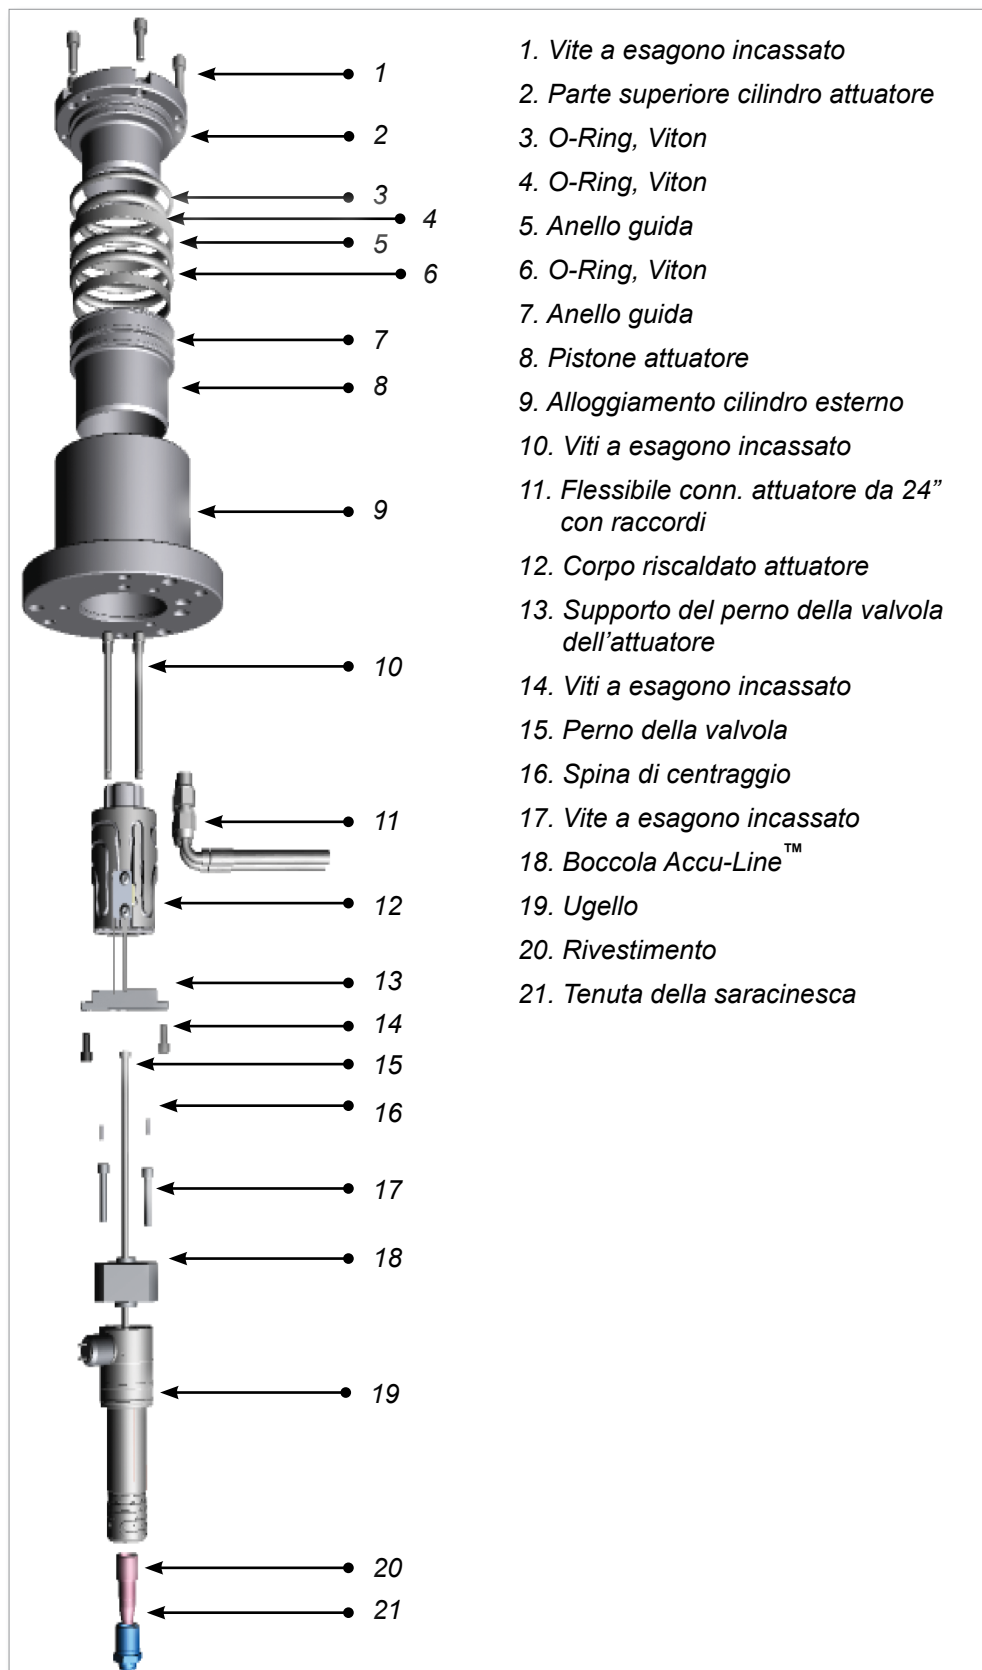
Assemblaggio del corpo Centi Accu-Line™
